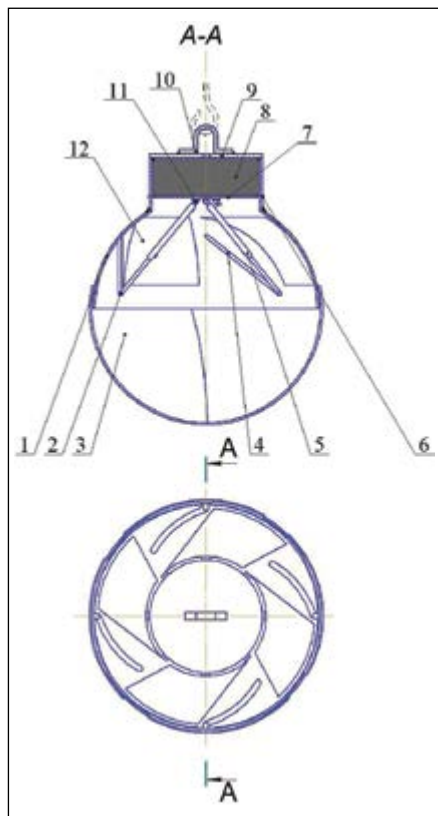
Многочелюстной грейфер со сферической рабочей поверхностью: 1 – каркас, 2 и 11 – шаровые шарниры, 3 – сферические челюсти, 4 – пазы, 5 – гидроцилиндры, 6 – болты, 7 – платформа, 8 – гидропривод, 9 – крышка, 10 – проушина, 12 – окна
